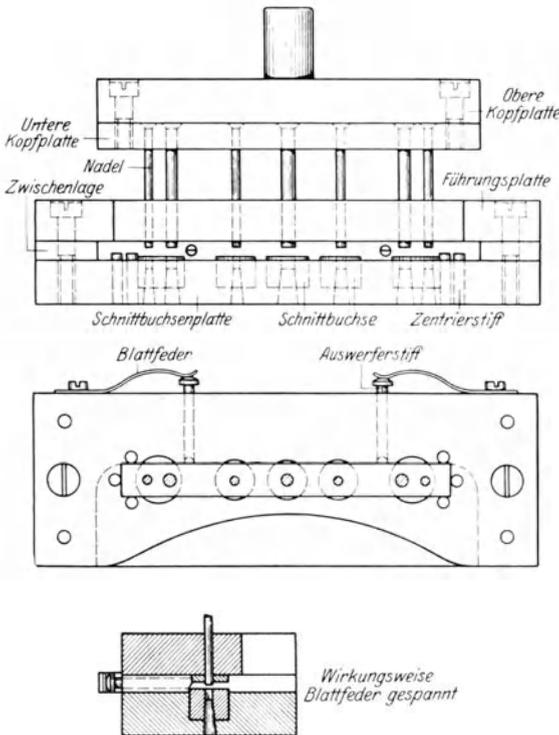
Lochwerkzeug mit Teilauswerfer.
